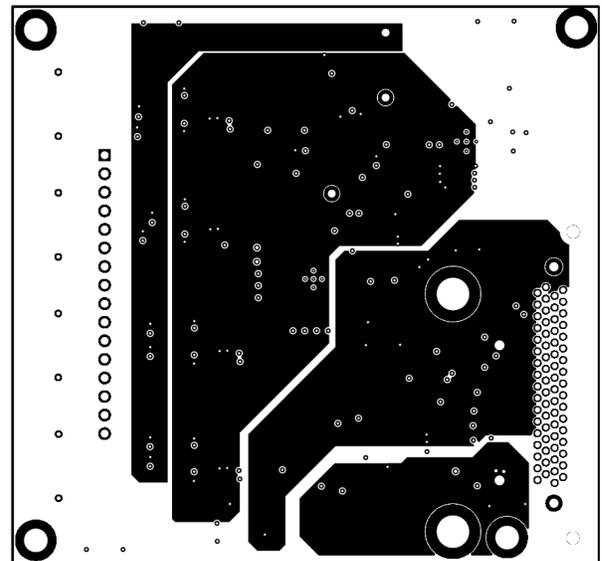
ADS8332EVMV2 PCB 第 3 层 : 电源平面
